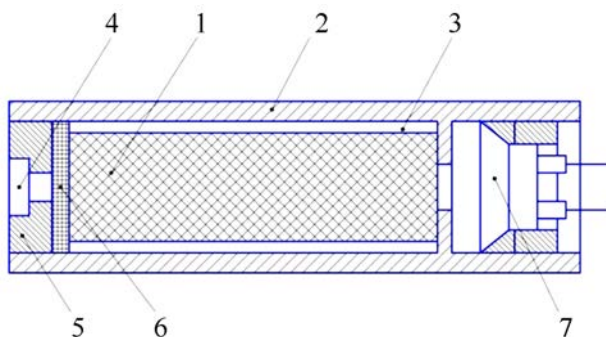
Конструктивная схема пиротехнического газогенератора: 1 – газогенерирующий заряд; 2 – корпус; 3 – зазор; 4 – канал вывода газа; 5 – гайка; 6 – фильтрующий элемент; 7 – инициирующее устройство
